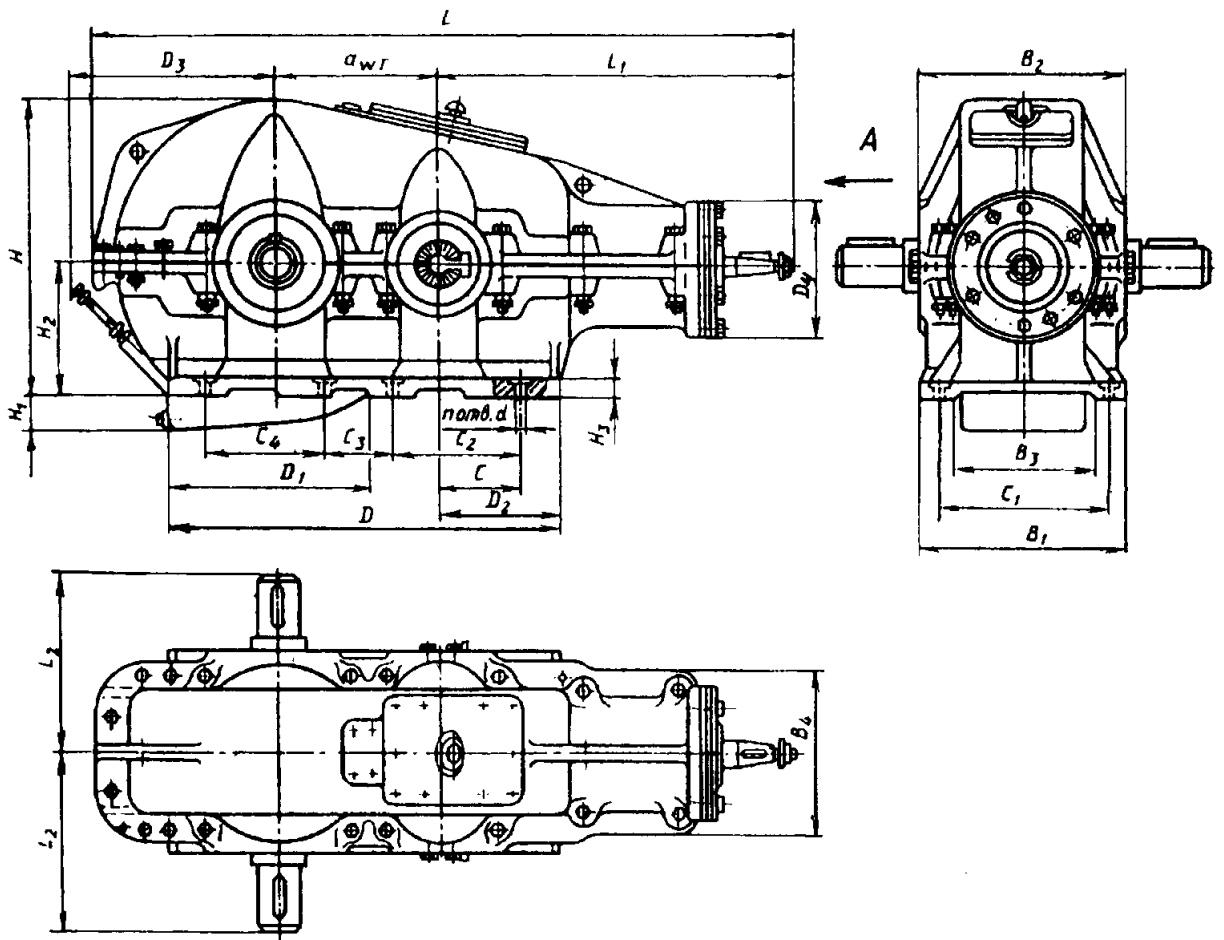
Коническо-цилиндрический двухступенчатый редуктор КЦ1 – 200[22]
